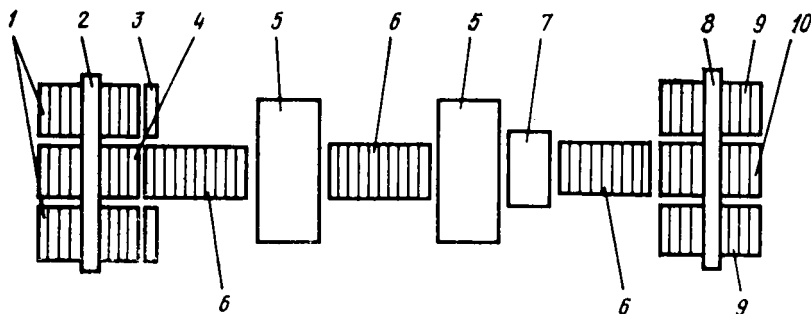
Схема автоматической линии МКШ1 калибровки щитовых деталей:
